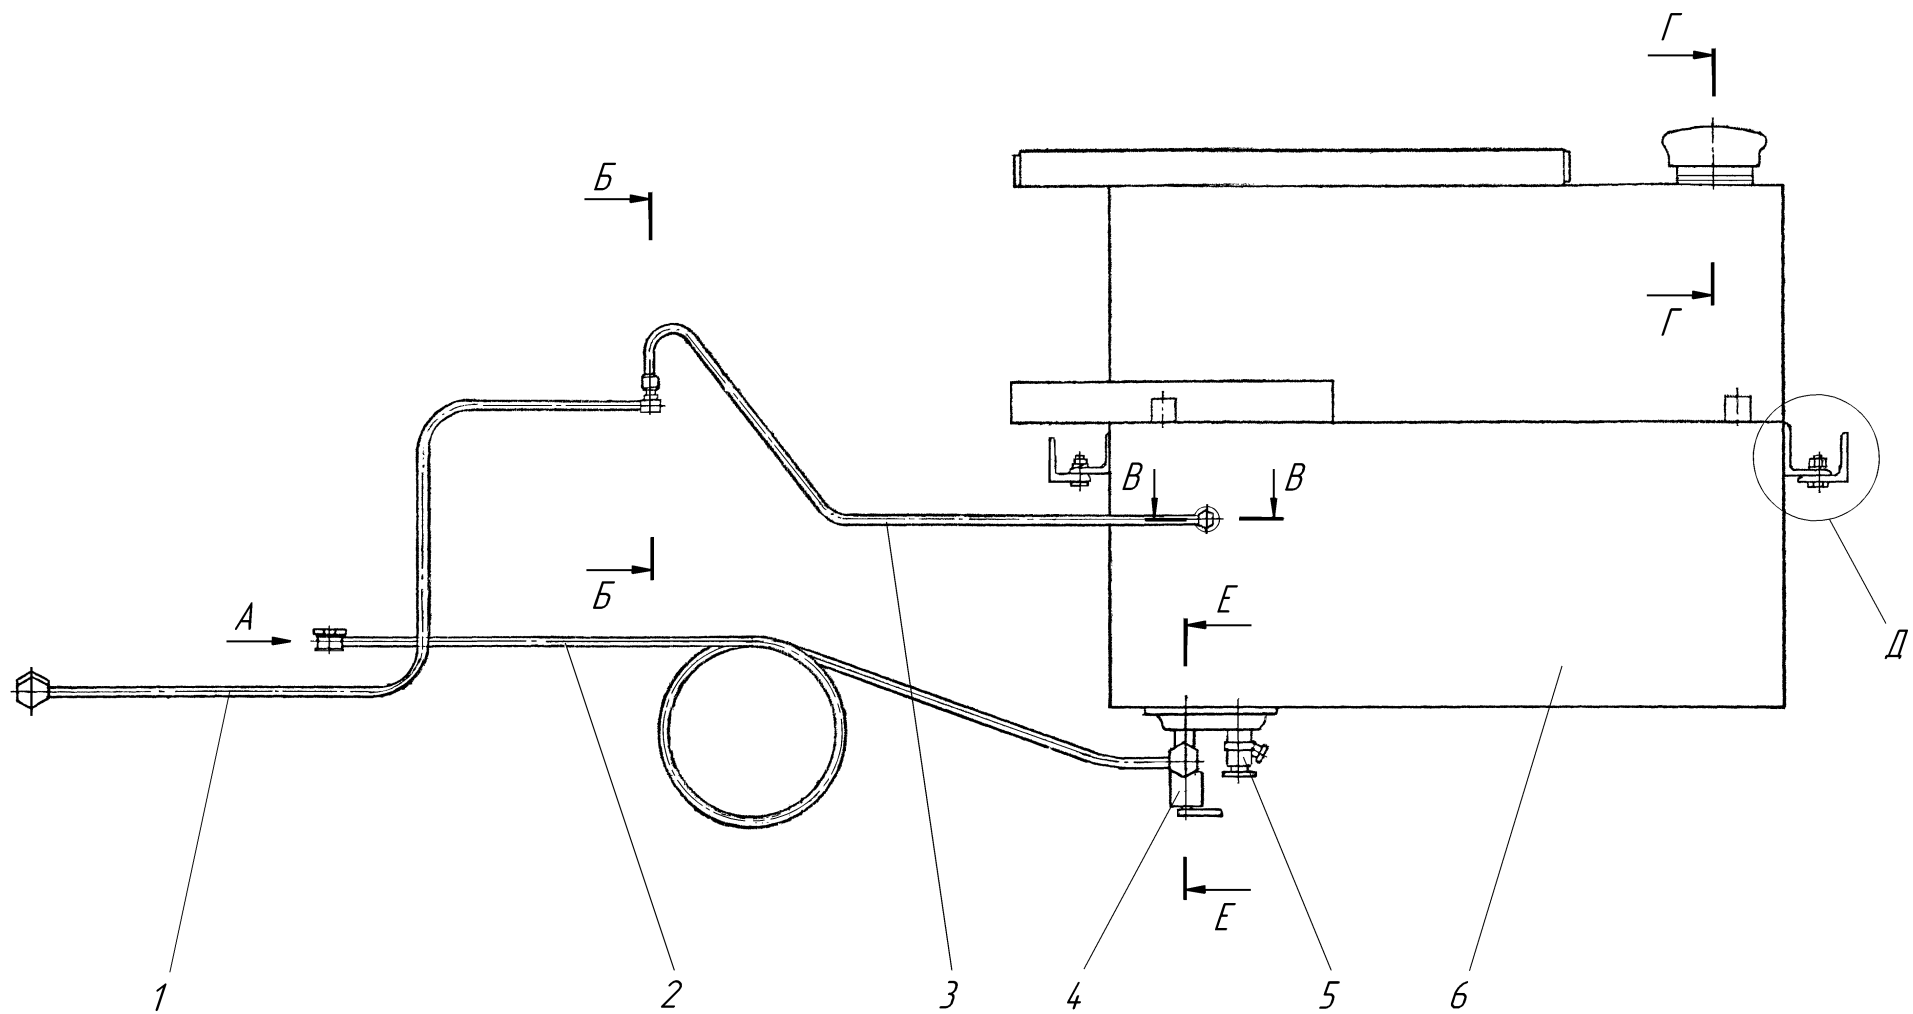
Установка бака топливного 665.06.00.00.000
